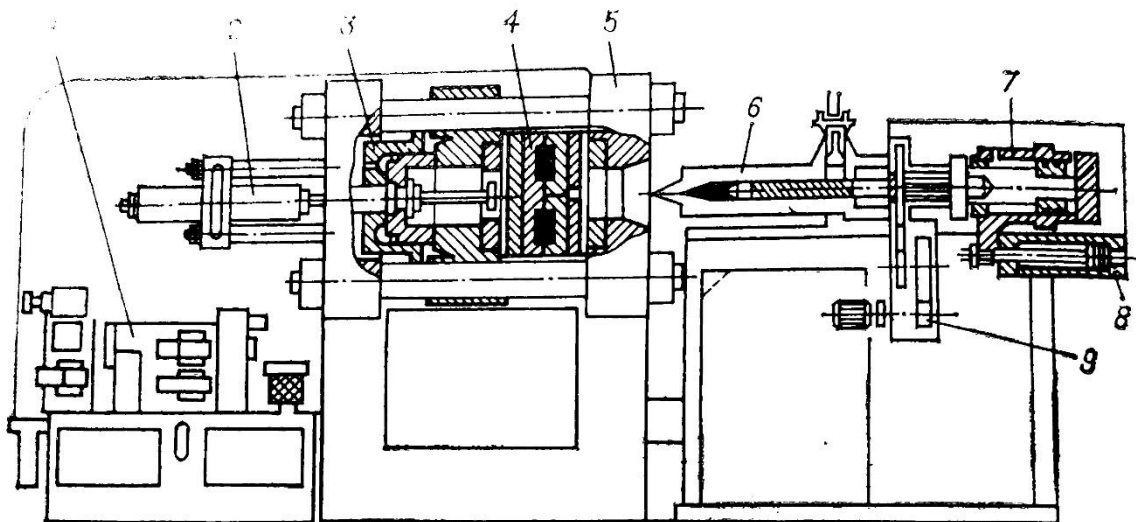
Горизонтальна литвева машина черв'ячно-плунжерного типу: 1 гидропривод; 2 цилиндр перемещения траверсин; 3 цилиндр змикання форми; 4 - ливарна форма; 5 - пресовий вузол; 6 інжекційний вузол; 7 - інжекційний цилиндр; 8 - гідроциліндр інжекційного вузла; 9 - привід обертання черв'яка
